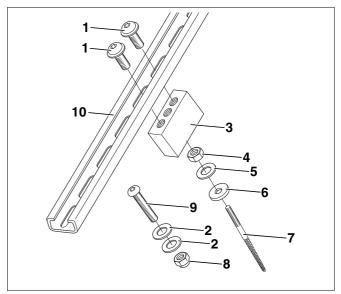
Conteúdo do fornecimento do conjunto de montagem para colectores planos
